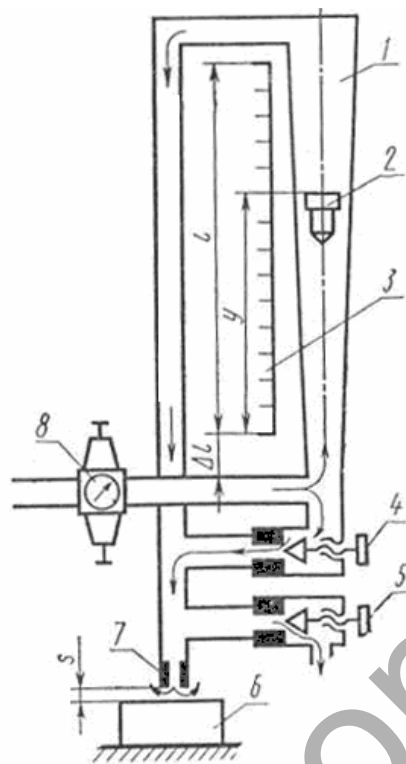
Схема пневматического прибора с ротаметром
